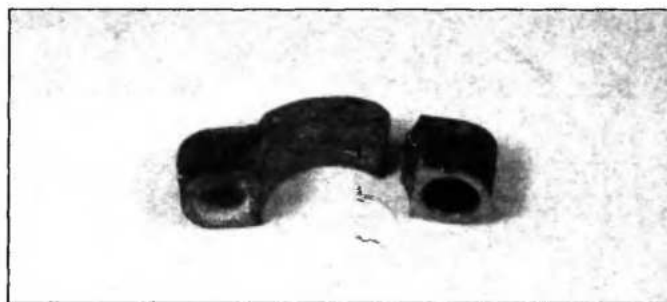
Поломка крышки подшипника распределительного вала из-за перегрева в режиме масляного голодания
